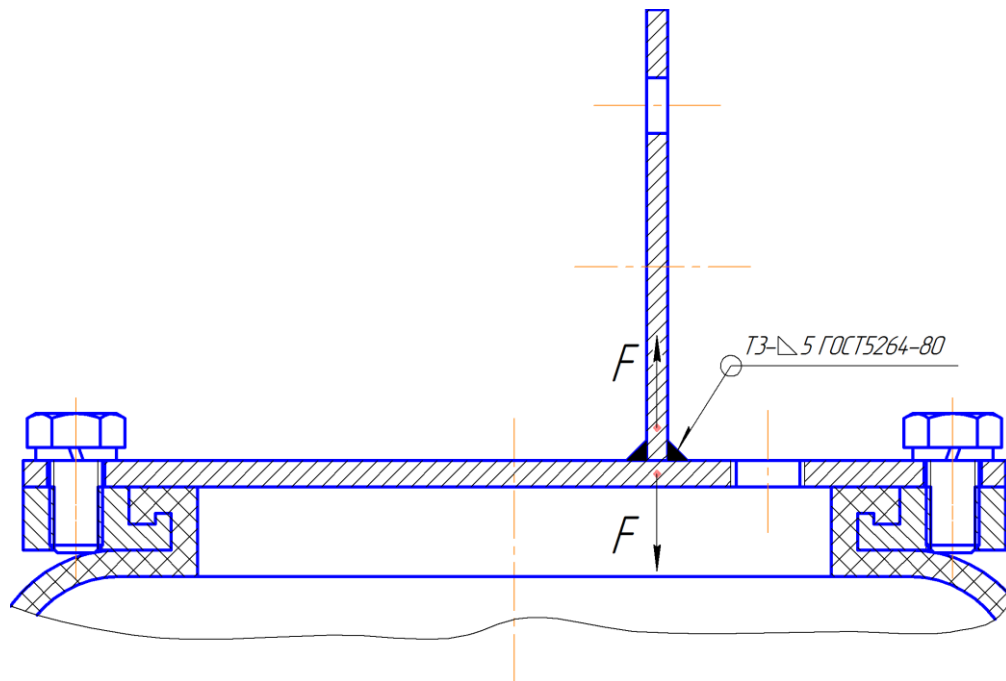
Расчётная схема сварного шва крепления кронштейна к крышке верхней
